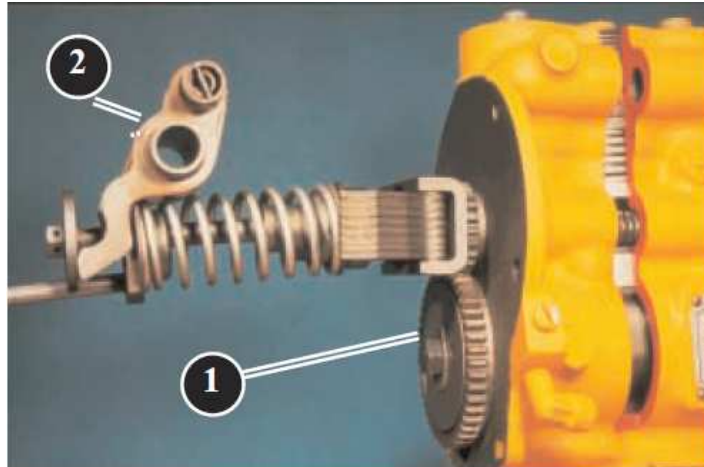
Engranajes de mando del regulador y palanca de control.
